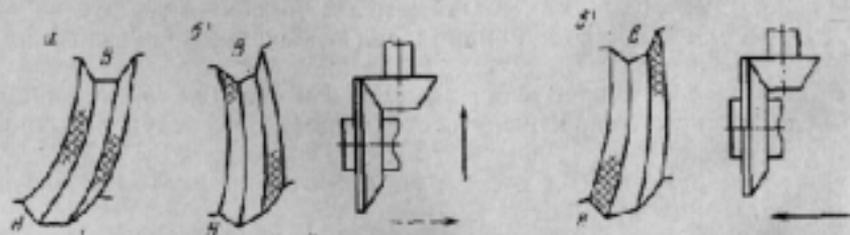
Расположение пятна контакта на зубьях ведомой шестерни главной передачи:
